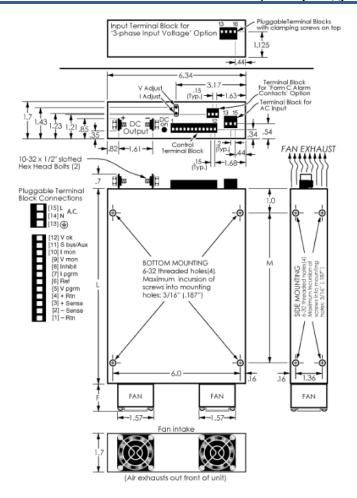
Acopian W110LT650D2P Габаритный чертеж
